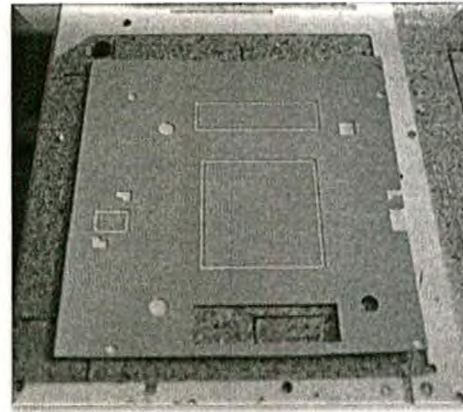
Máquina CNC y capa de LTCC cruda mecanizada.
